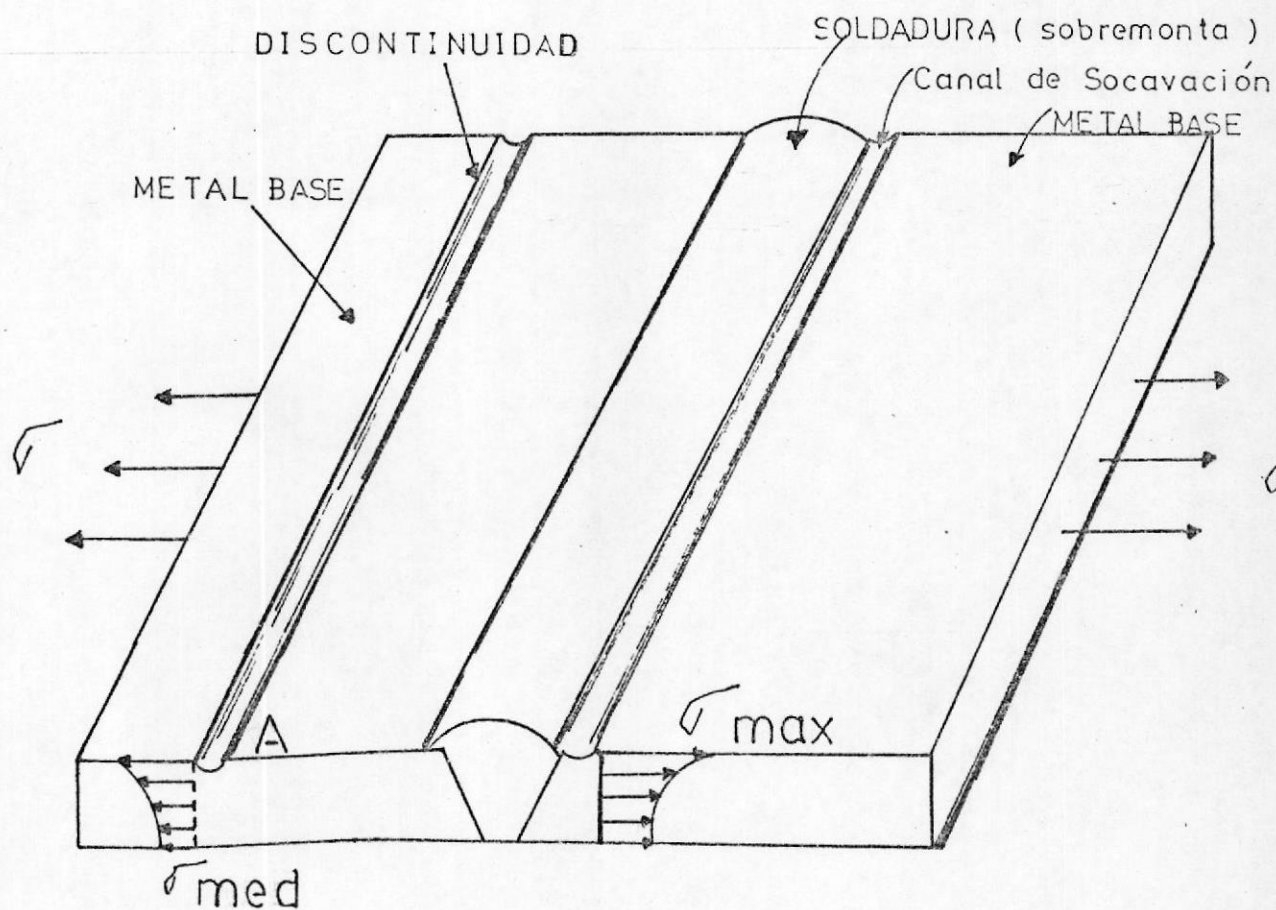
SOCAVACION O MORDEDURA EN UN PROCESO DE SOLDADURA AL ARCO (10).
